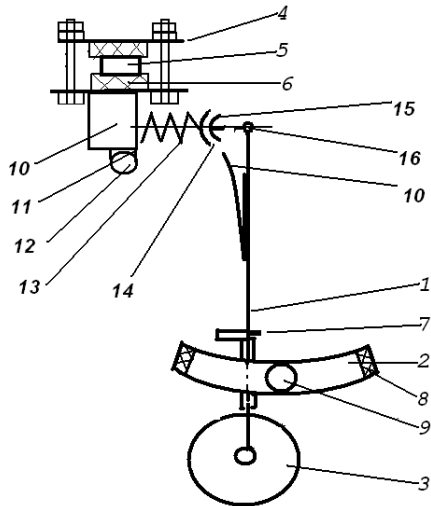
Конструкцію ДГК комбінованого ударно-маяткового типу
